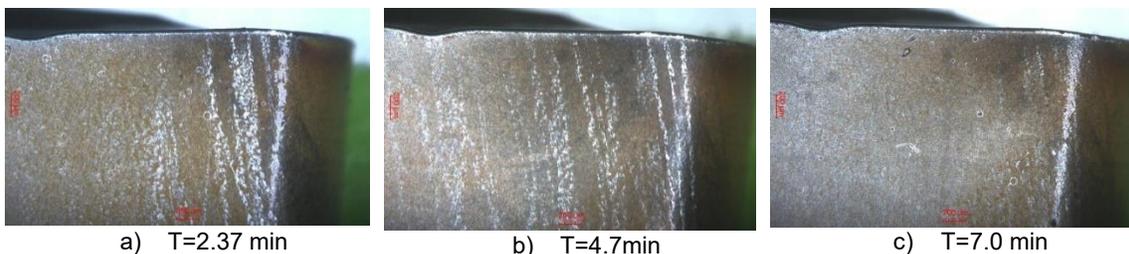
Desgaste en el flanco de la herramienta en condiciones de corte con MQL.
